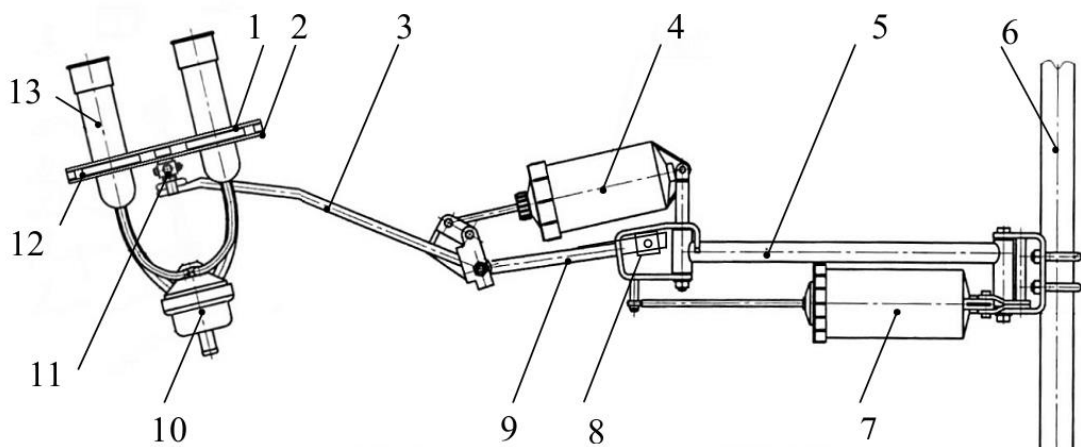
Загальний вигляд удосконаленого маніпулятора для машинного доїння корів: 1 – фіксатор стаканів доїльних верхній; 2 – фіксатор стаканів доїльних нижній; 3 – штанга підтримуюча; 4 – пневмокамера підтримуючої штанги; 5 – опорна стійка; 6 – стійка станка; 7 – пневмокамера стійки станка;
